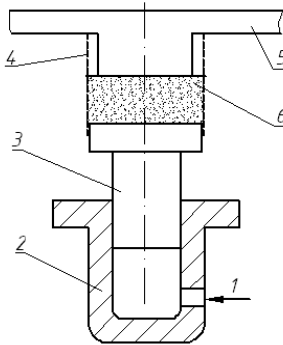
Схема гідравлічного преса: 1 – подача рідини для робочого ходу плунжера; 2 – силовий циліндр; 3 – плунжер; 4 – зерний циліндр; 5 – плита; 6 – пакет з мезгою
